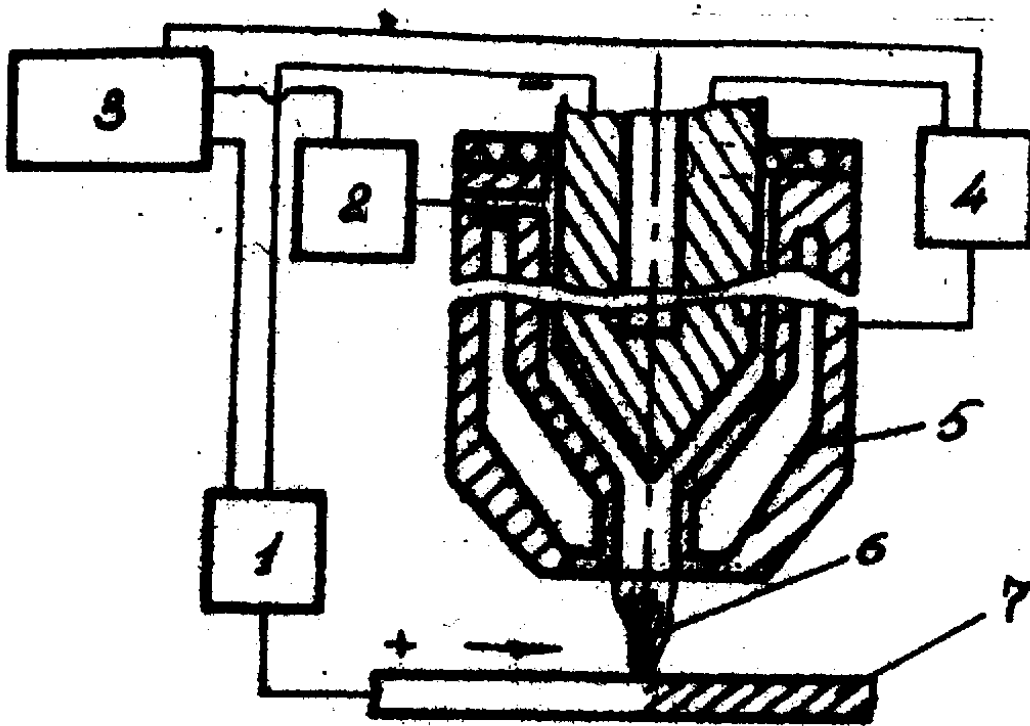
Структурна схема установки для плазмової обробки матеріалів
